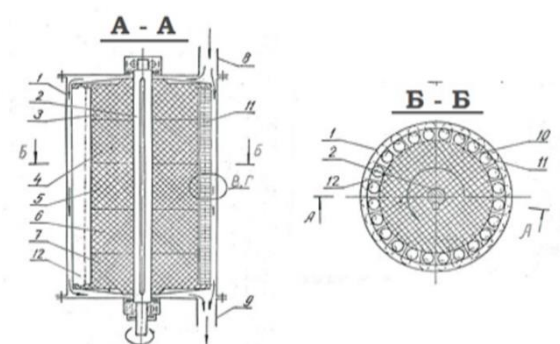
Схема каскадной энергонапряженной измельчительной машины «МЭ-3D»: 1 - корпус мельницы; 2 – вал ротора; 3,4,5,6,7 – секции ротора; 8 – входной канал; 9 – выходной канал; 10 – толкающая пластина; 11 - мелющее тело; 12 – футеровка корпуса
